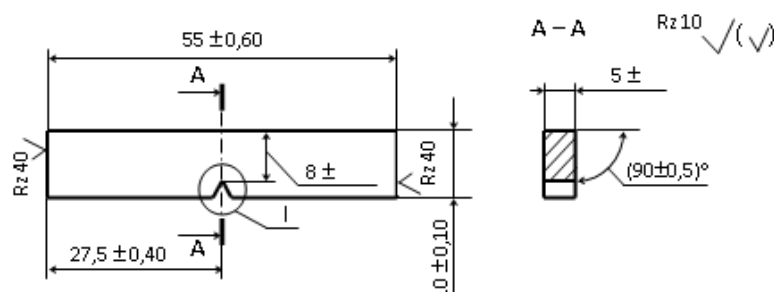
Форма и размеры образцов для испытаний на ударный изгиб по ГОСТ 6996
